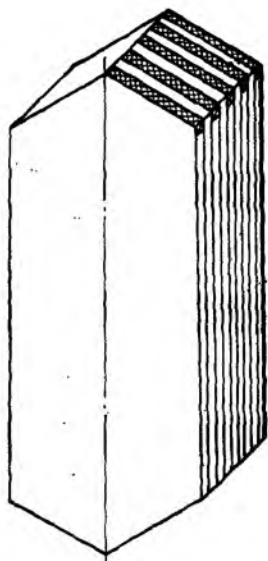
Сварной блок (пакет) пластинчатого конденсатора
